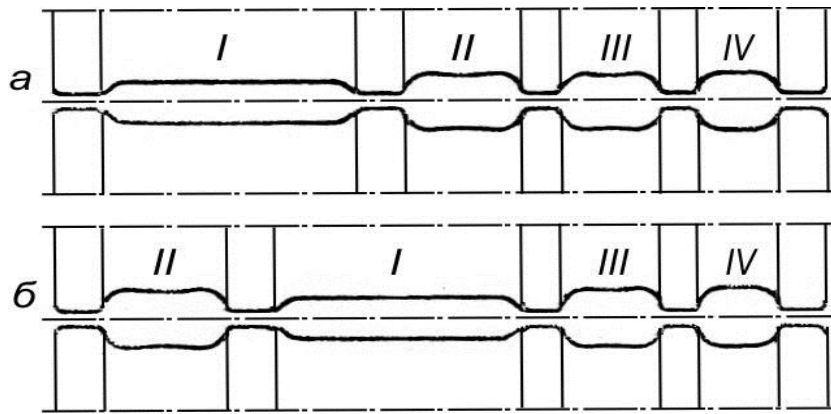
Схемы расположения калибров на валках блюминга:
